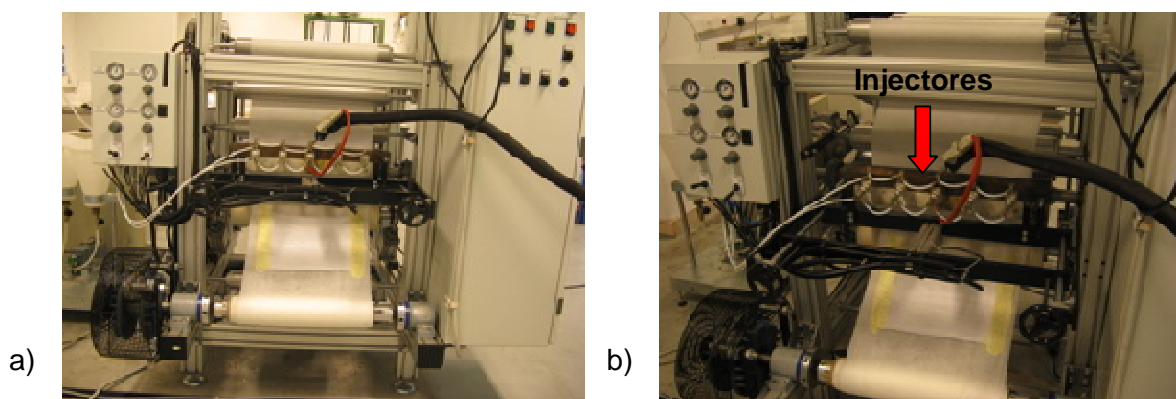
a) Imagem real da máquina do hot melt; b) Pormenor dos injectores de adesivo.
